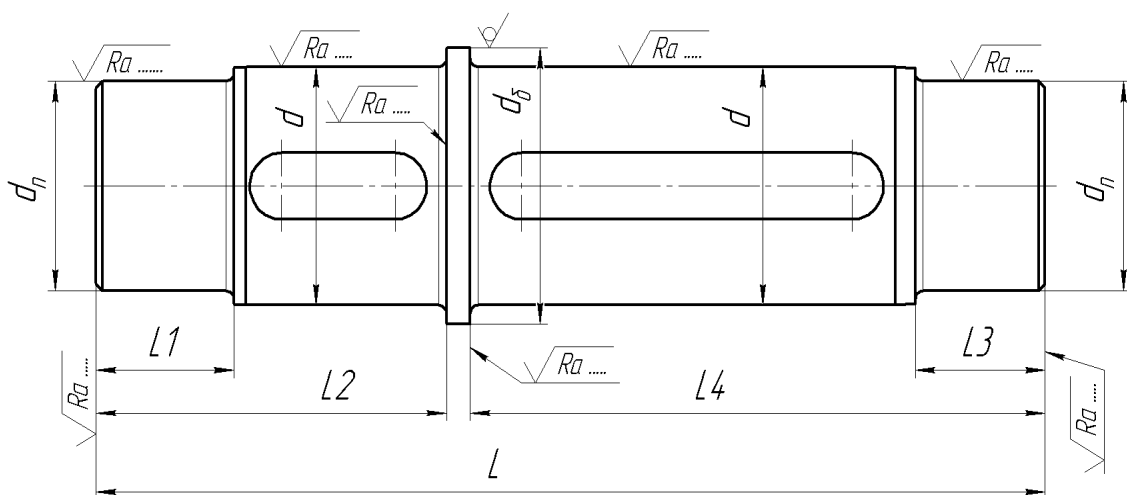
Схема розташування шорсткості поверхонь на кресленні проміжного вала.
